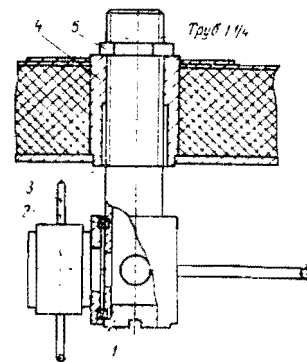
Общий вид головки моечной резервуара марки Г6-ОМГ-25:
